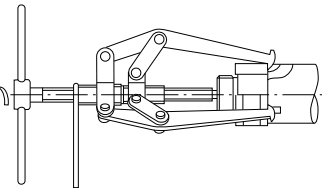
Demontage des Innenrings mit Abziehwerkzeug (2)
